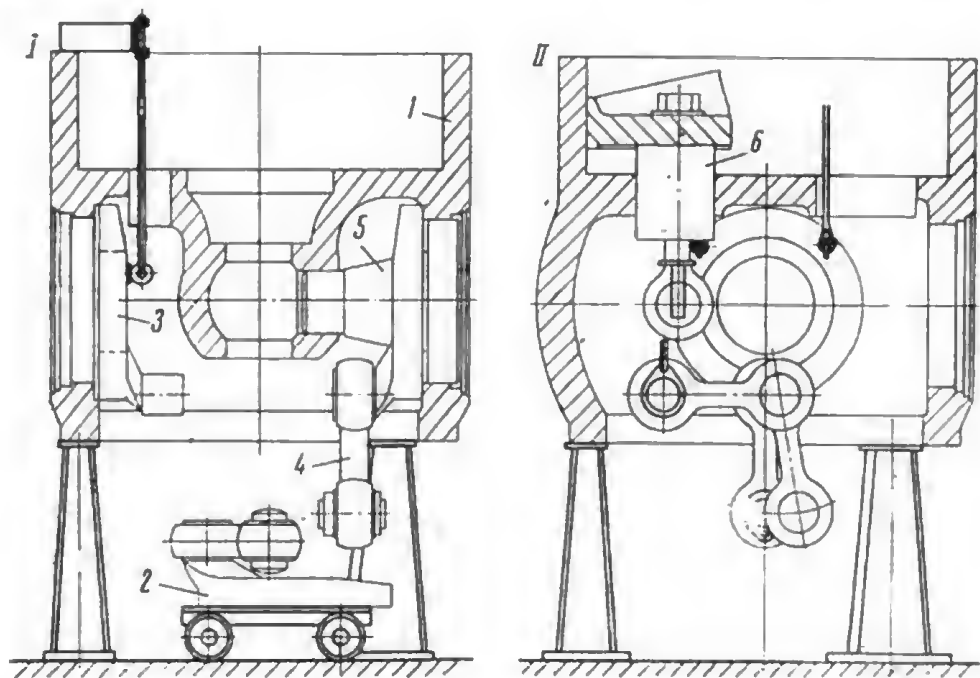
Сборка механизмов поворота бескостовинного рабочего колеса.
